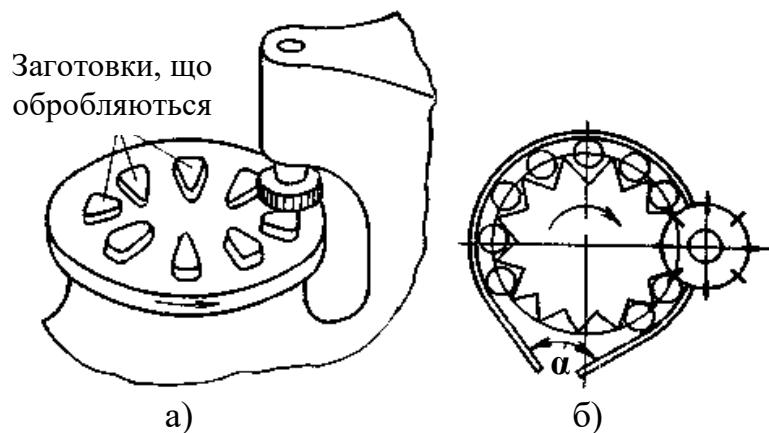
Схеми багатомісної паралельно-послідовної обробки з безперервною зміною заготовок:
